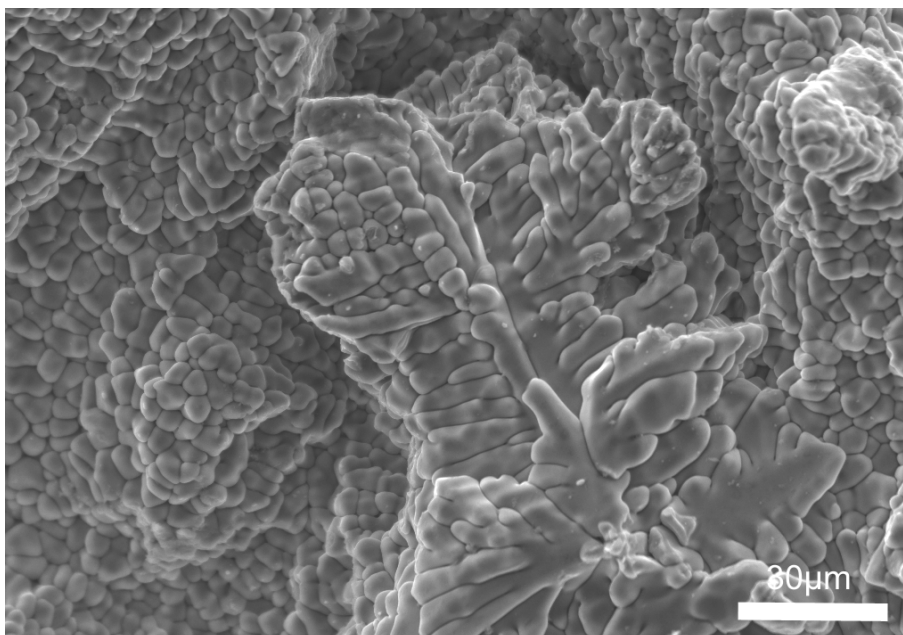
dendrite sur faciès de rupture en fissuration à chaud
